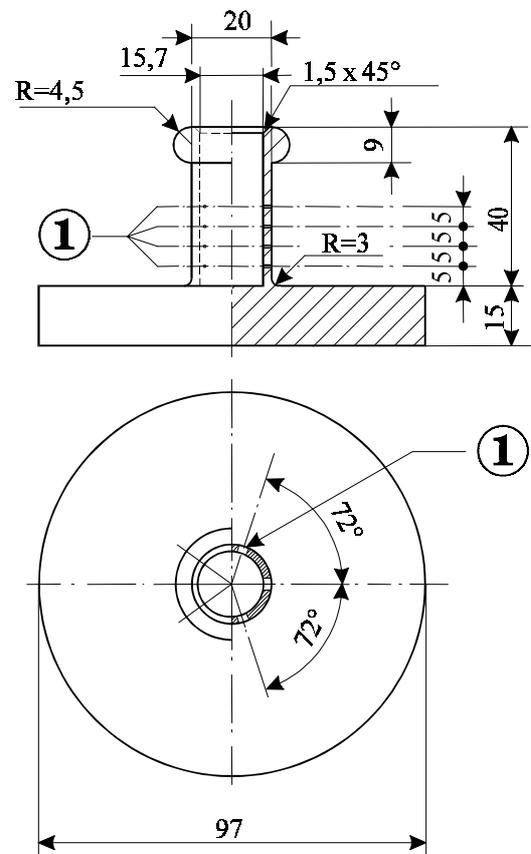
Hohler Bronzezylinder, einseitig verschlossen.
